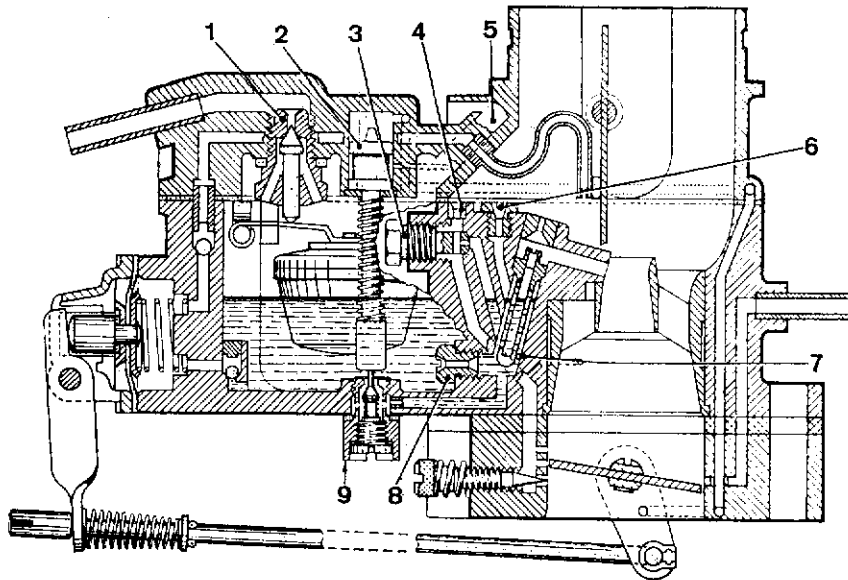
Coupe du carburateur Solex 35 PDSI - 6
